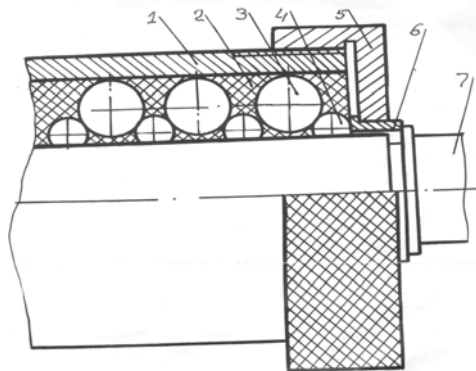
Конструкція патрона з шариковою обоймою, розташованою в пружному наповнювачі
